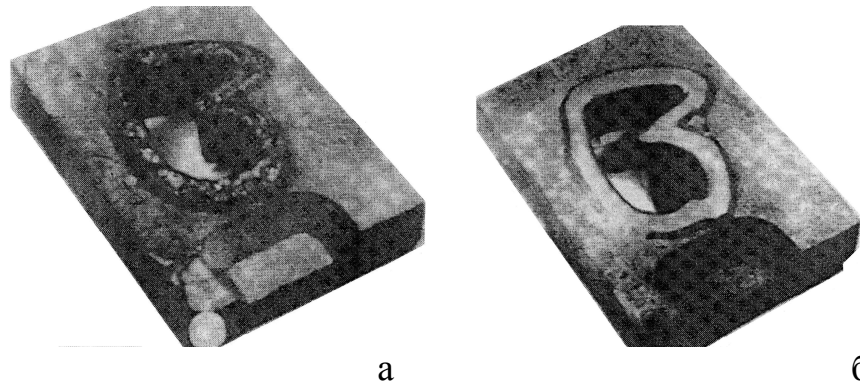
Обрезная матрица из стали 45 с упрочненной рабочей поверхностью: а – после наплавки; б – после двухкратного отпуска и механической обработки
